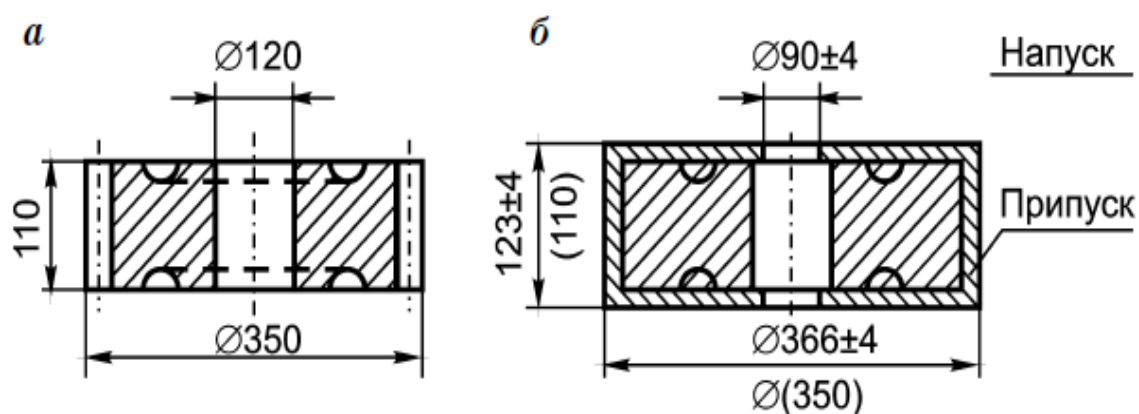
Чертежи: а – готовой детали, б – поковки [1]
